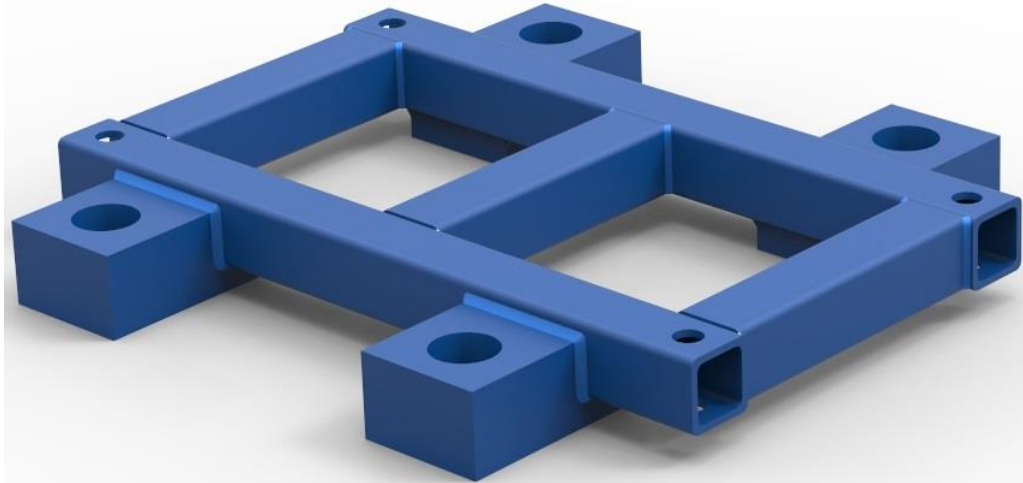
Konstrukční provedení zdvihacího mechanismu
